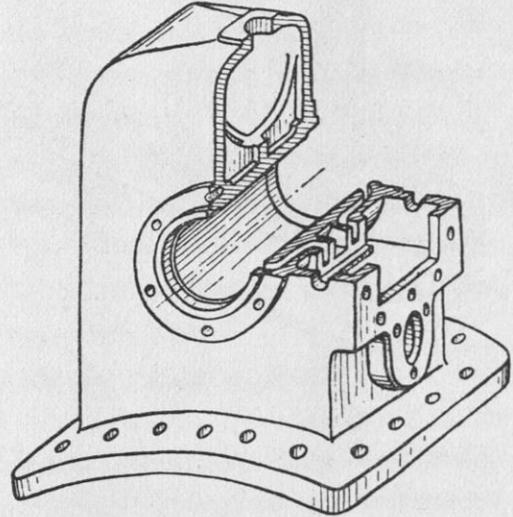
Spätere Ausführung des Domzylinders bei Satteldampfmaschinen
